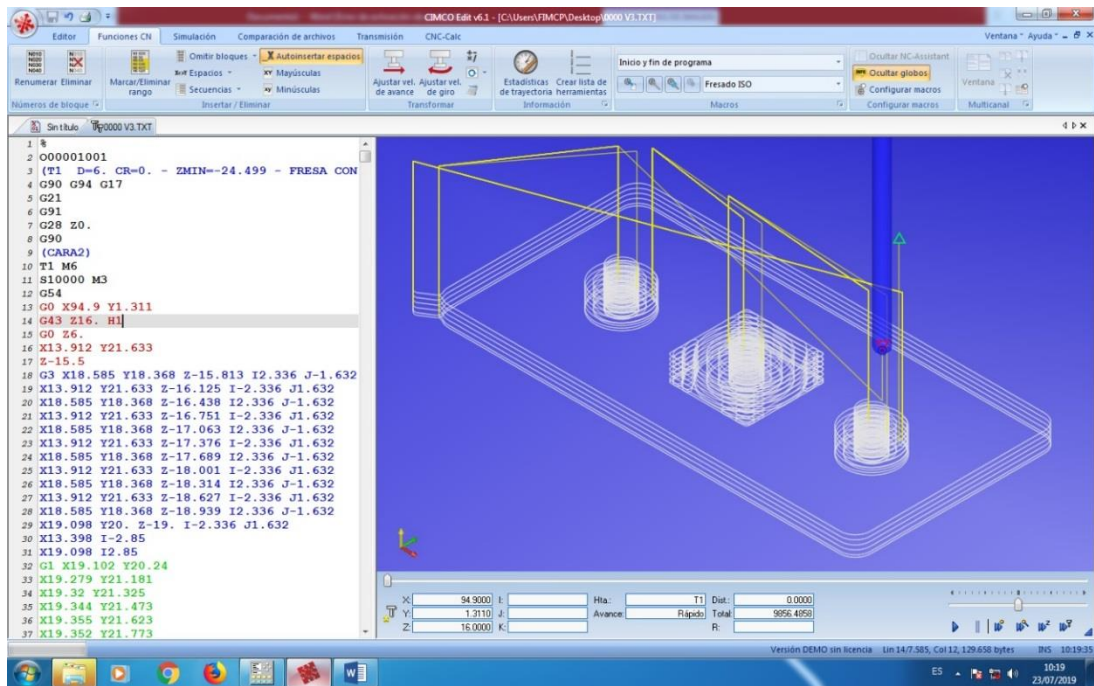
Desplazamiento de la fresa durante el maquinado [el autor]
